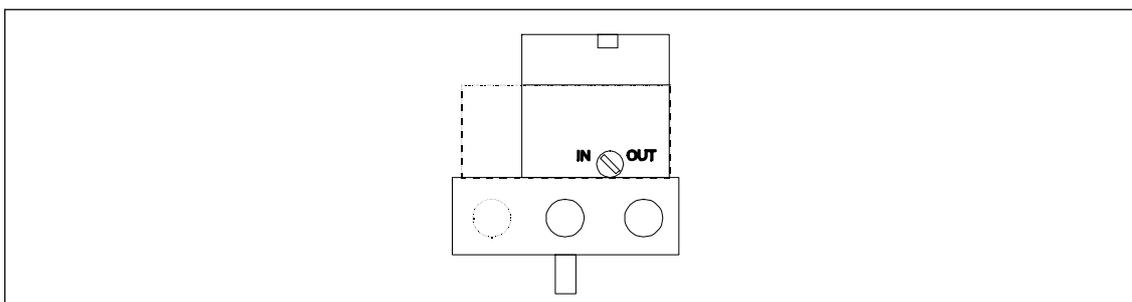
Comutador do ar de lavagem no bloco de válvulas, vista geral do posicionador no lado de conexão pneumático com tampa aberta
